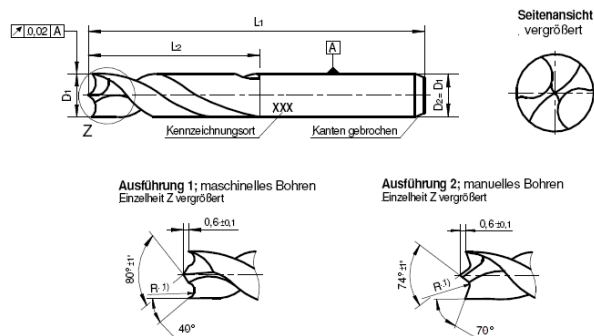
VHM-Werkzeug – Sichelbohrkopf
